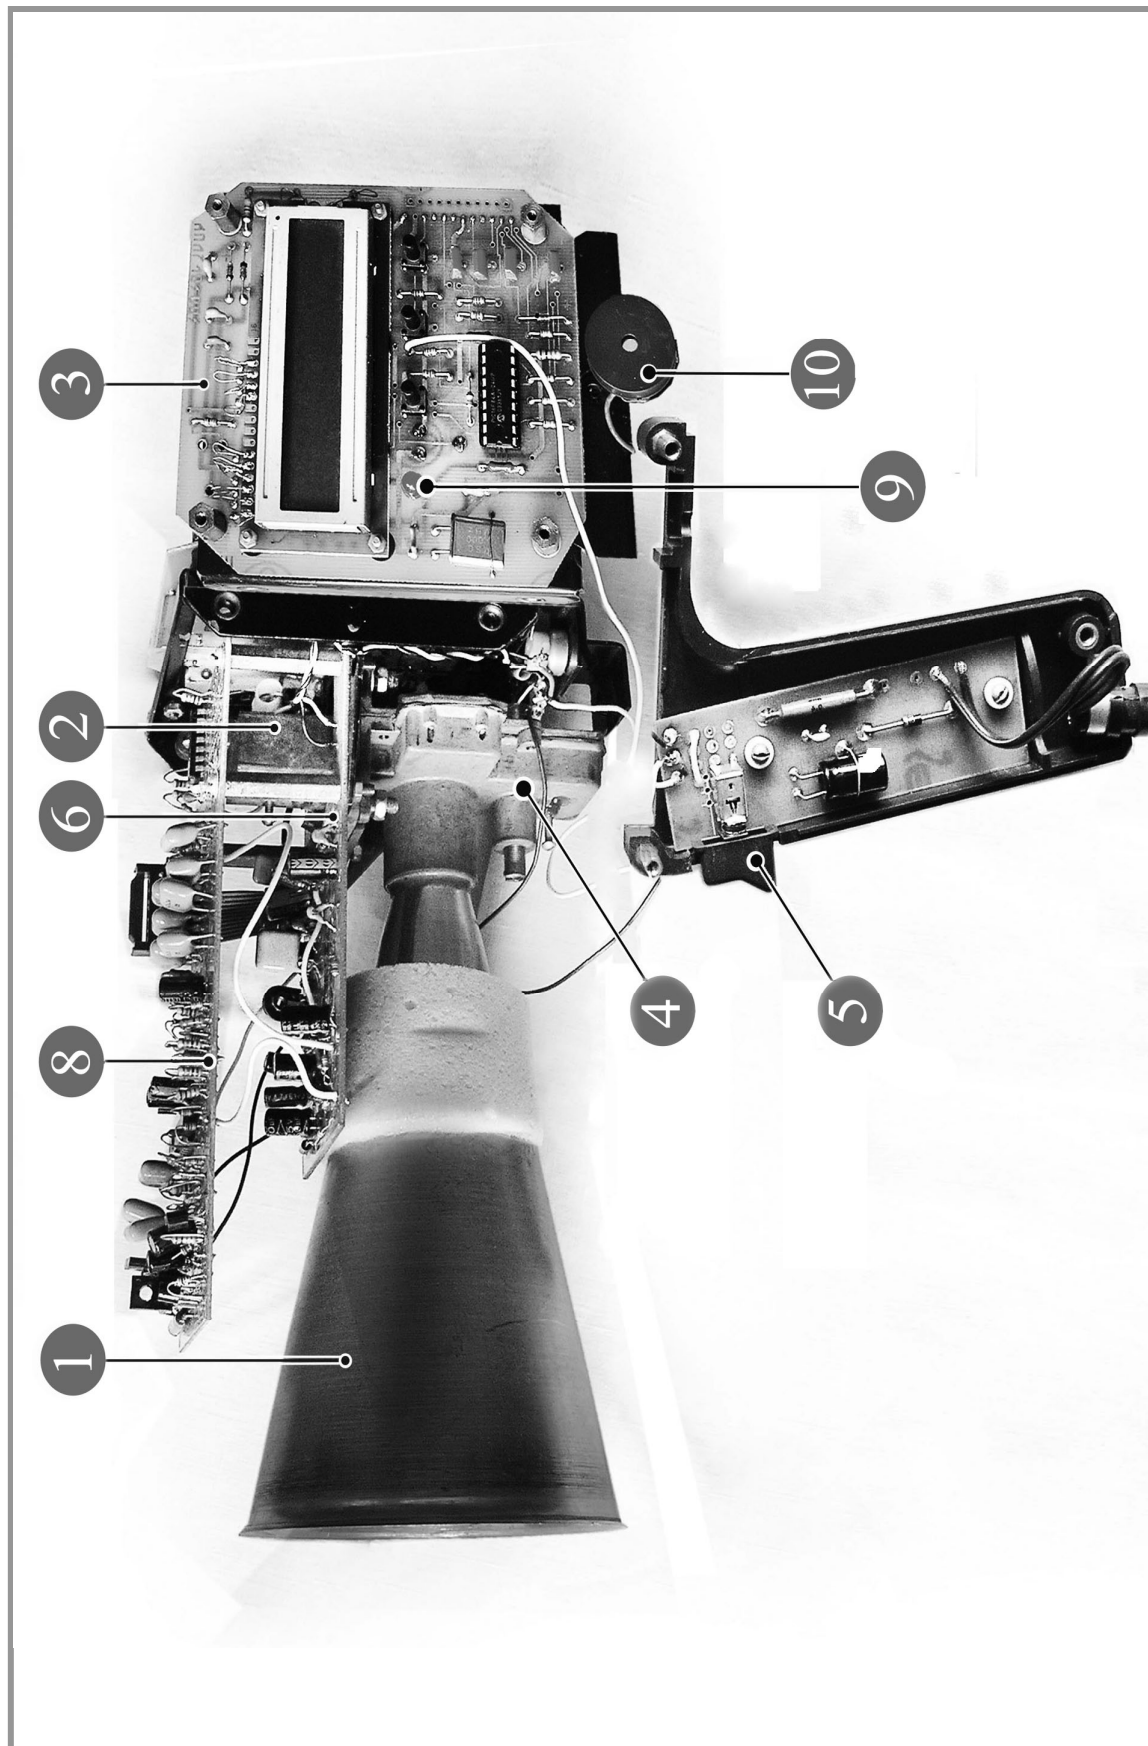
Конструкция измерительного блока прибора "Барьер 2-2М"
